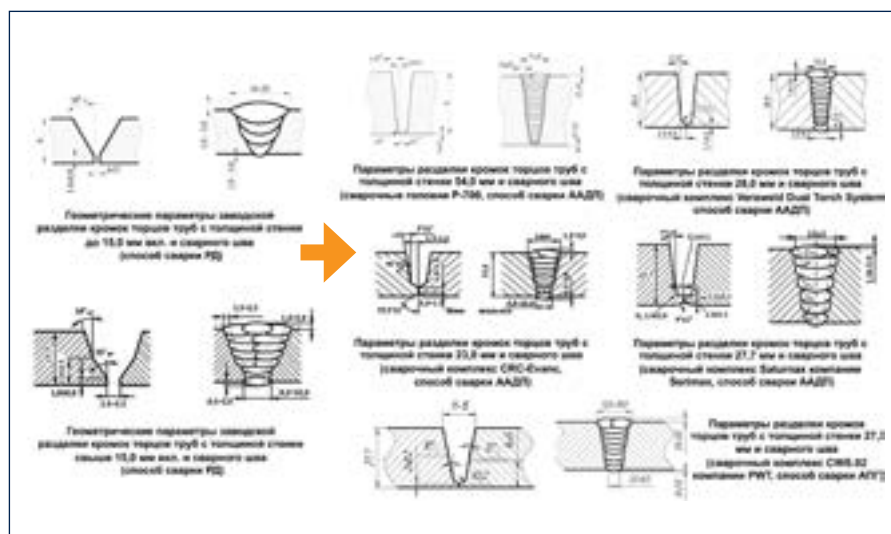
Геометрические параметры разделки торцов кромок труб и сварного шва (в сравнении по способам сварки)
